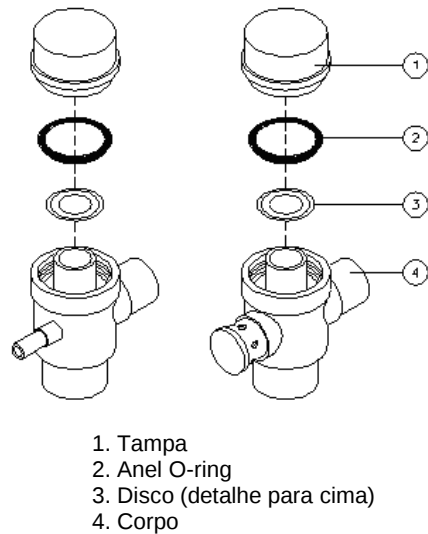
Montagem das válvulas inspiratória e expiratória.
